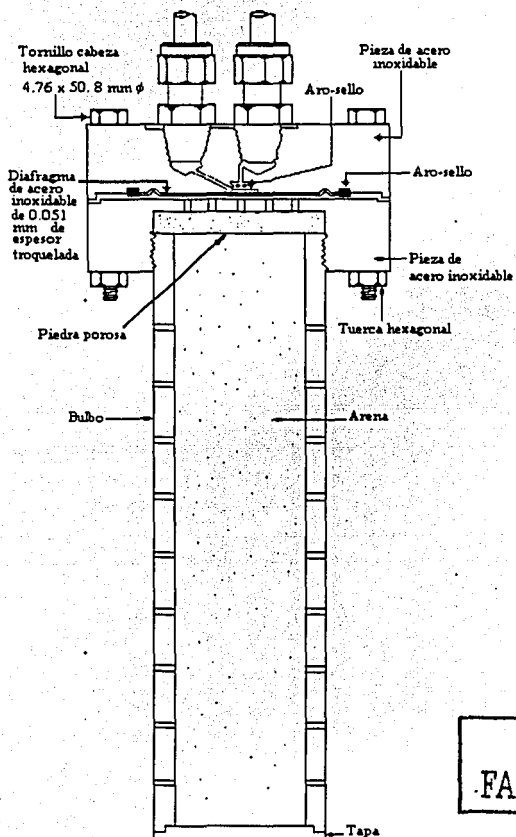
Piezómetro neumático tipo CFE.
